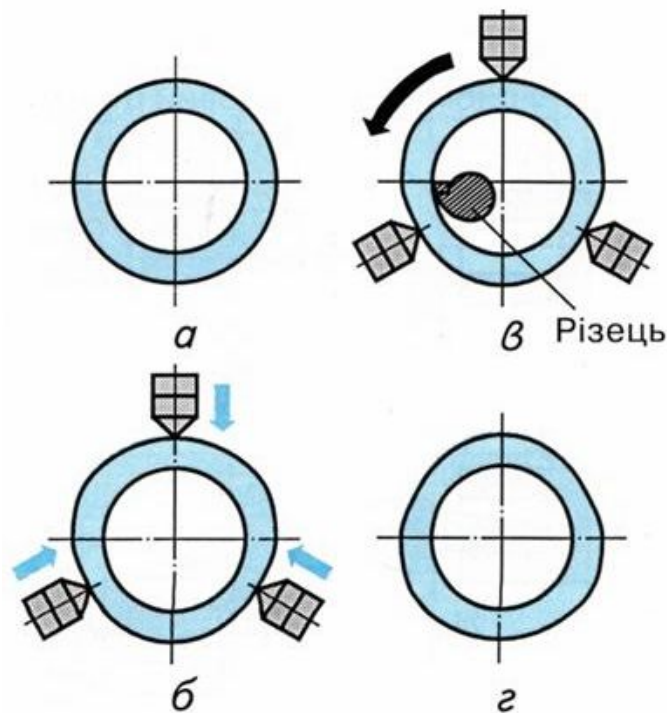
Схема деформування тонкостінної втулки після затискання в трикулачковому патроні: а-трубчаста заготовка; б-затискання заготовки; в-розточування; г-вигляд деталі після розтискання кулачків
